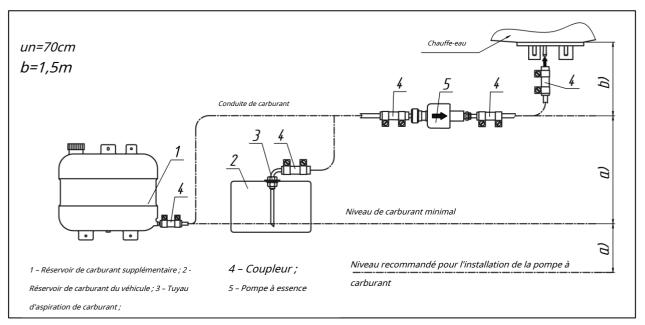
Position en hauteur de la pompe à carburant dans le système de carburant
